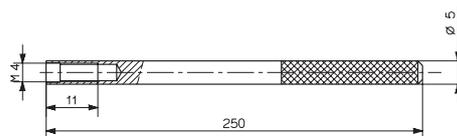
Ausziehwerkzeug für Blindsensor Typ 1319
